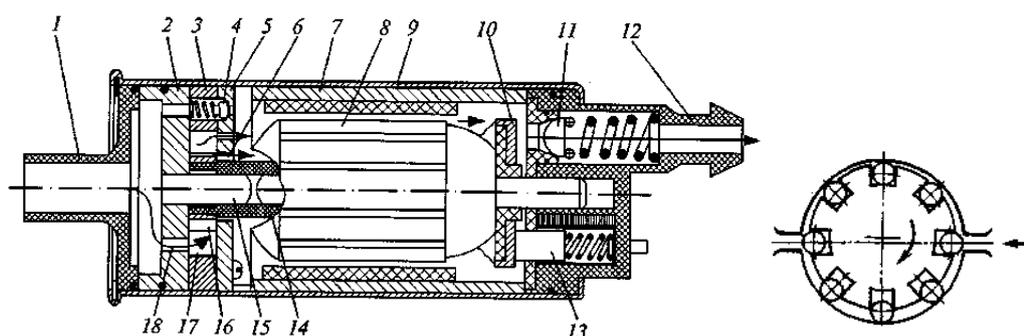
Топливный насос: 1, 12 - штуцеры; 2 - основание; 3 - статор; 4, 11 - клапаны; 5 - крышка; 6, 18 - каналы; 7, 9 - корпусы; 8 - якорь; 10 - коллектор; 13 - щетка; 14 - муфта; 15 - вал; 16 - сепаратор; 17 - ролик
